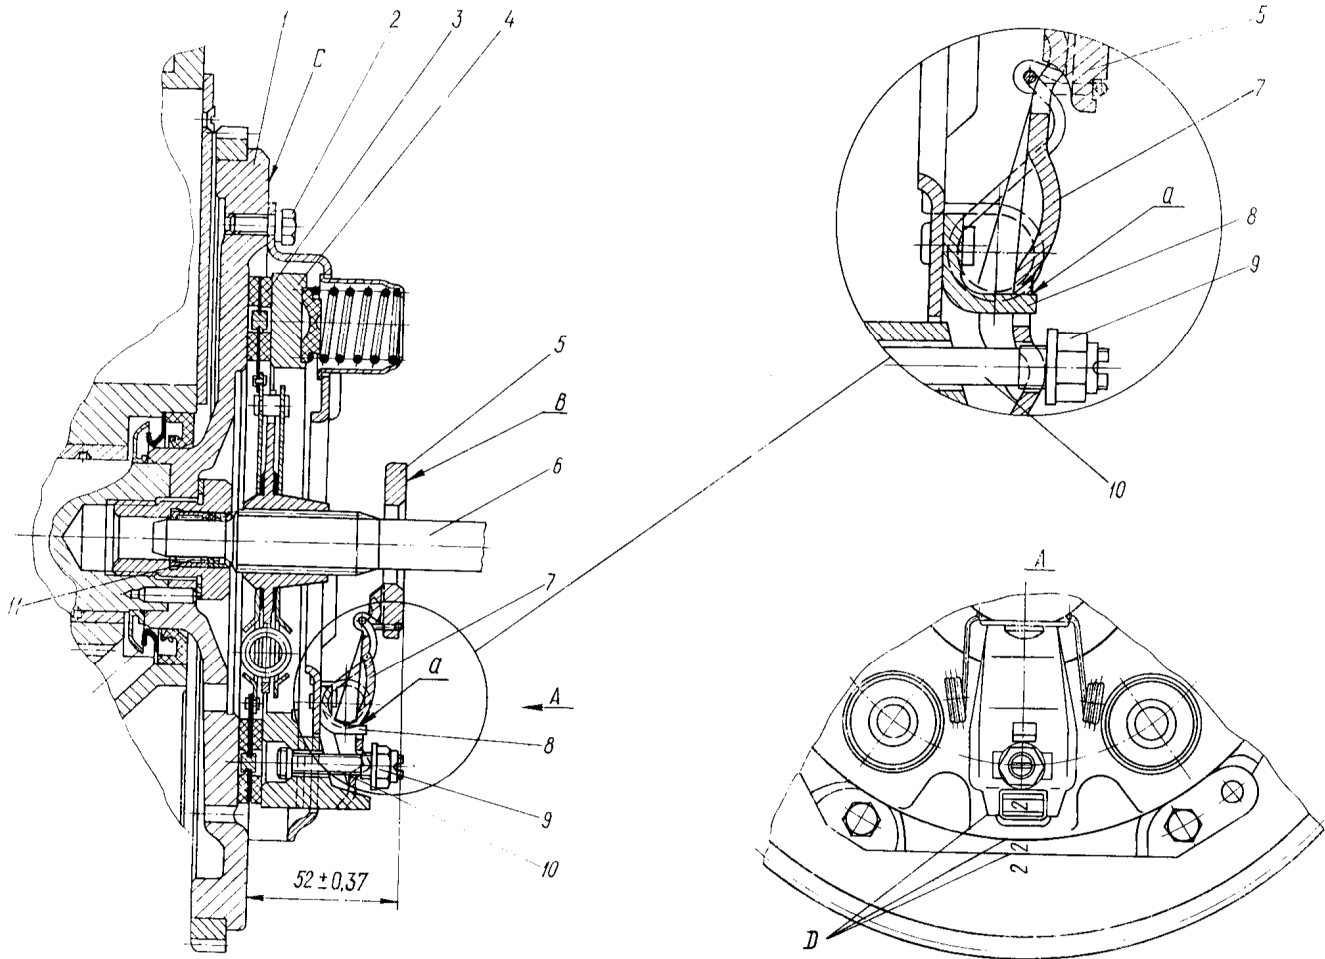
Установка ведомого диска сцепления с помощью оправки:
